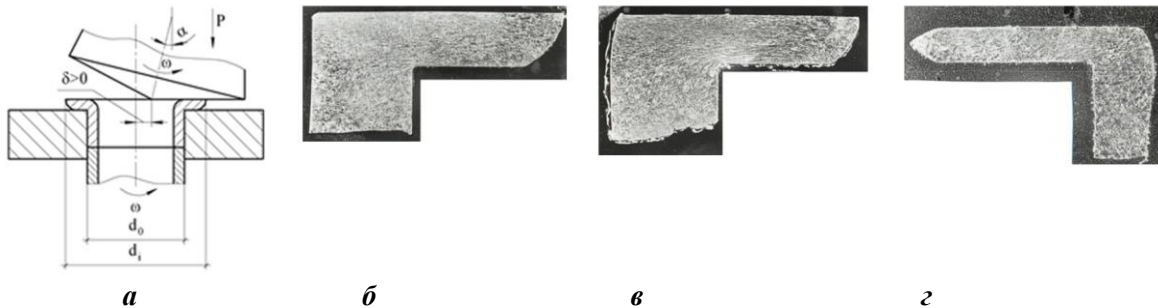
Схема висаджування зовнішнього фланця заготовки методом штампування обкочуванням а) і форми перерізу сформованого фланця б), в), з) в залежності від положення вершини валка
